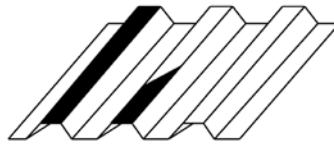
Схема нанесення клею на поверхні, що сполучаються
